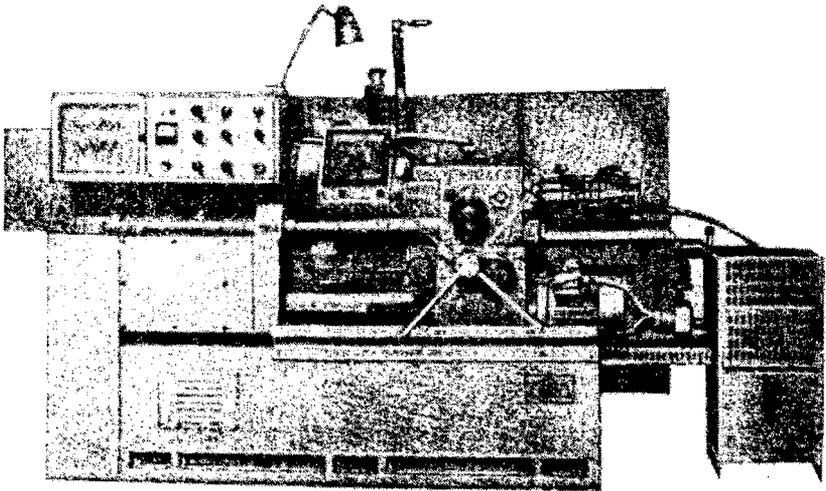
Токарно-револьверный станок 1Г340
